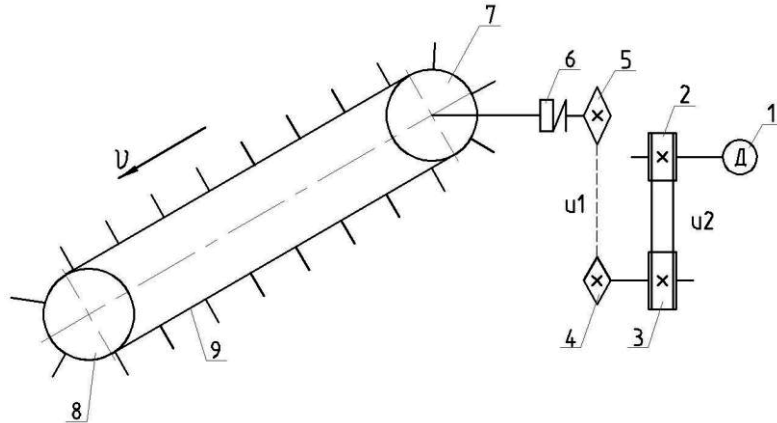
Кінематична схема скребкового конвеєра: 1 – двигун, 2, 3 – шкві пасової передачі, 4, 5 – зірочки ланцюгової передачі, 6 – муфта, 7 – приводна зірочка, 8 – приводна зірочка скребкового конвеєра, 9 – ланцюг зі скребками
